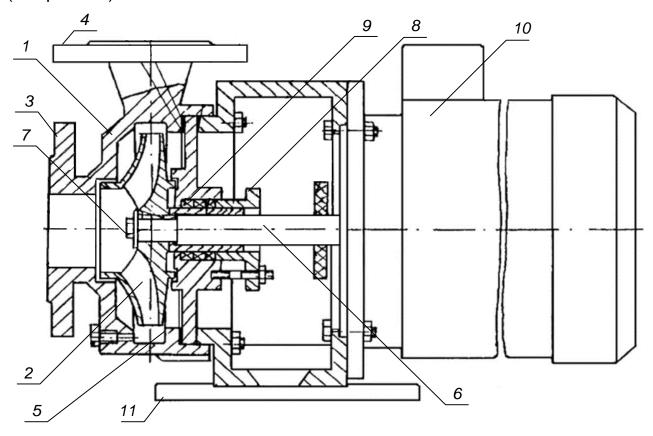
Конструкция насоса КМ: 1 — спиральный корпус; 2 — рабочее колесо; 3, 4 — всасывающий и напорный патрубки; 5 — уплотняющее кольцо; 6 — удлиненный конец вала; 7 — гайка; 8 — крышка сальника; 9 — набивка грундбуксы; 10 — вал; 11 — станина насоса
